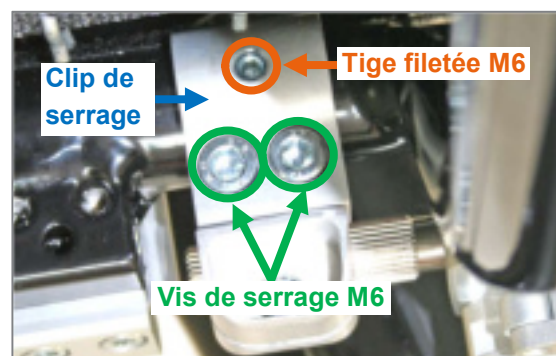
Tige filetée M6 et vis de serrage M6 pour le déplacement du clip de serrage sur le tube de châssis (vue du côté intérieur du produit)
